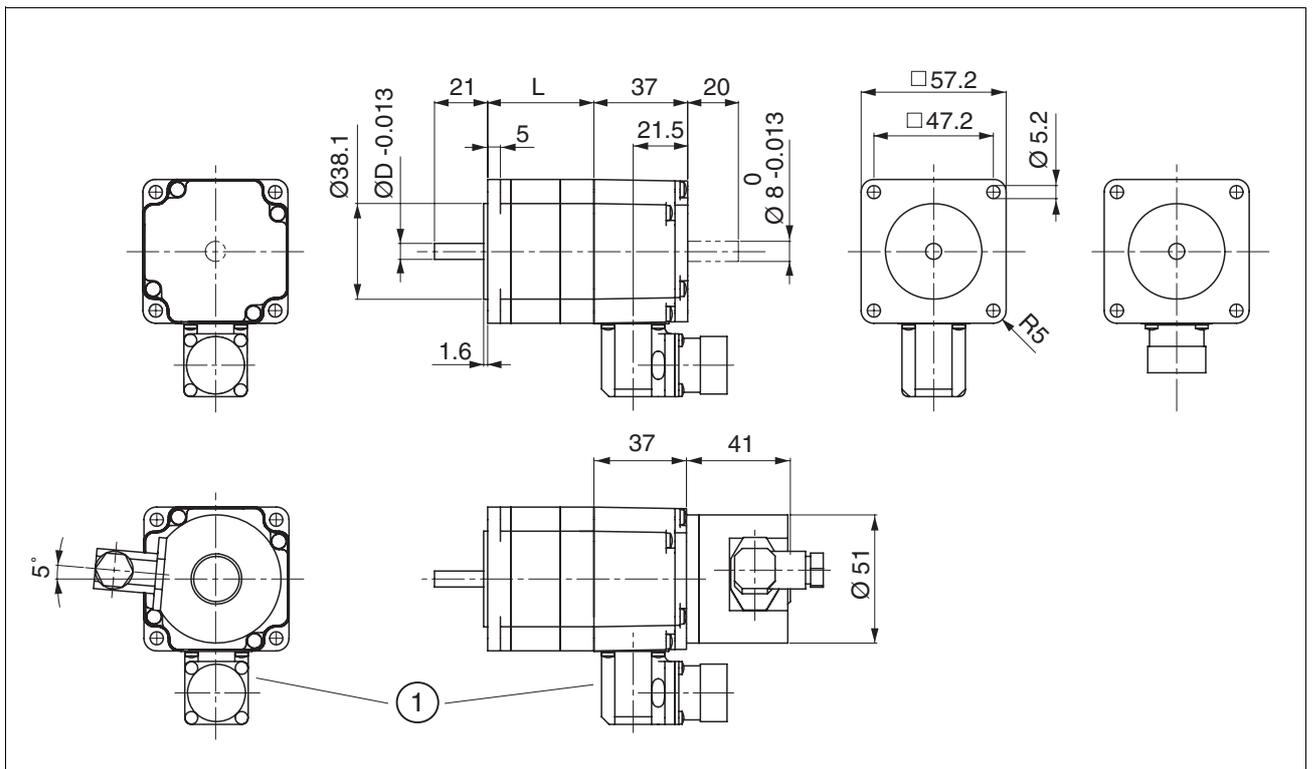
BRS36 Maßzeichnung Steckerausführung ohne Encoder
